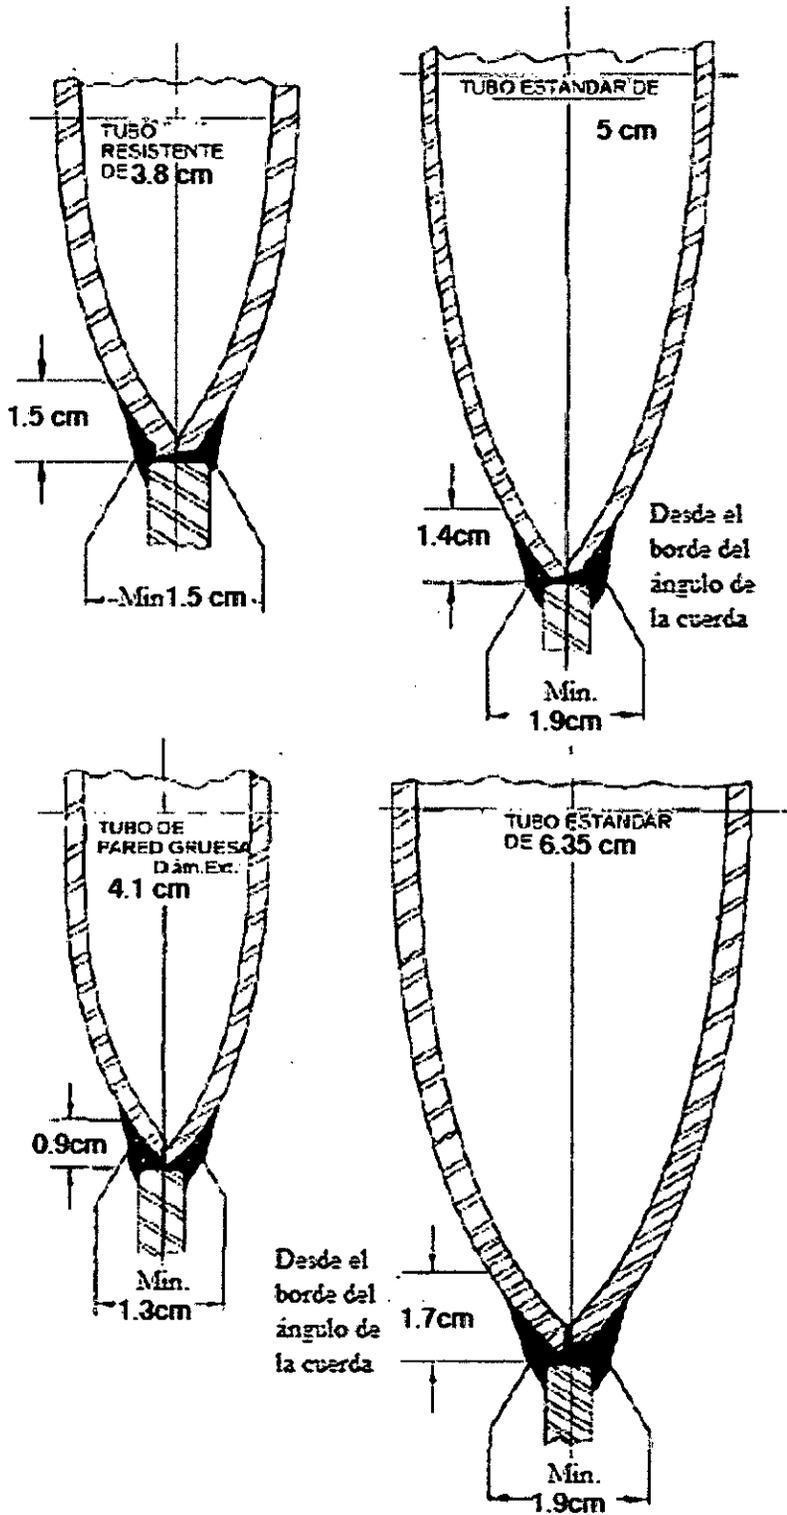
SOLDADURA DE MIEMBROS ANGULARES DE PLUMA.
